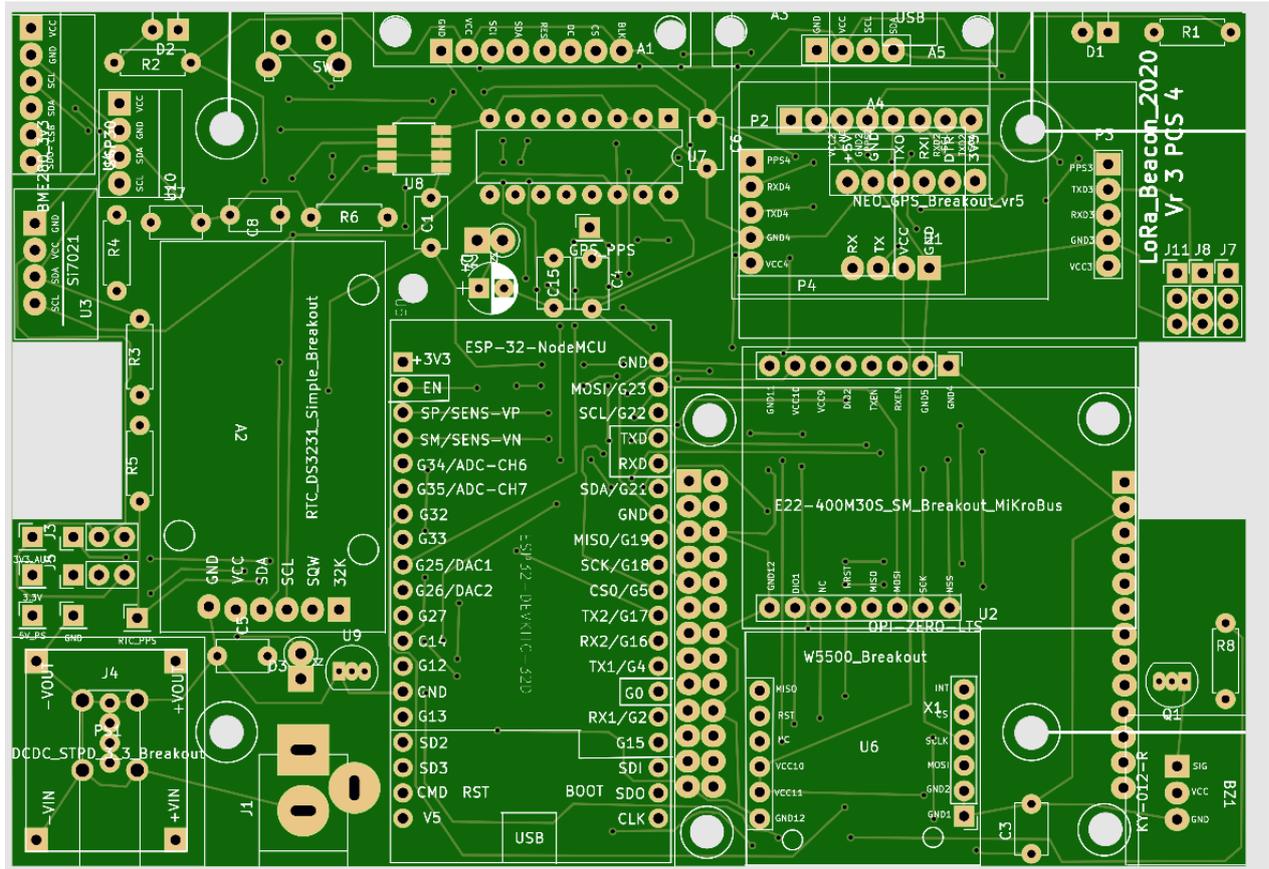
LoRa_Beacon_Vr 3 pcs 4 : foto lato superiore PCB
